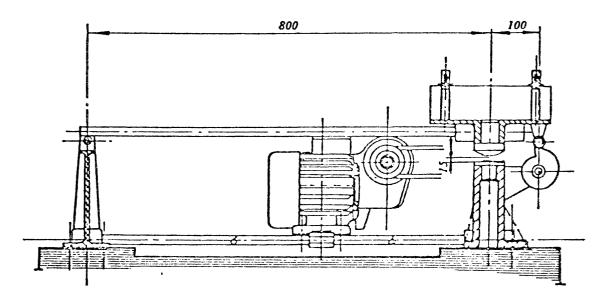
Compactadora de choques (ejemplo). Dimensiones en mm.
